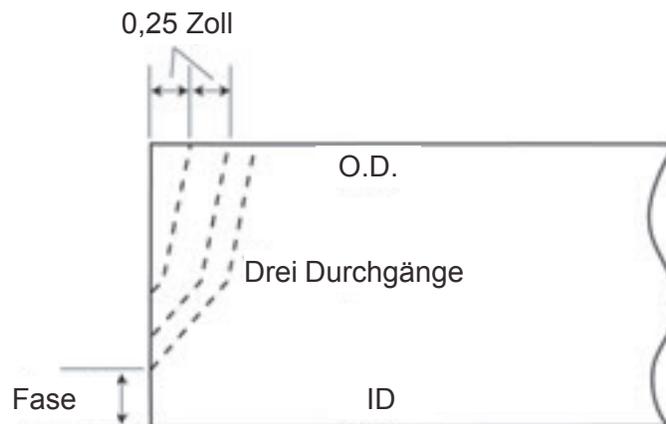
Drehen Sie die Kronenmutter, um die Spitze gerade hinter dem Rohraußendurchmesser zu positionieren.
